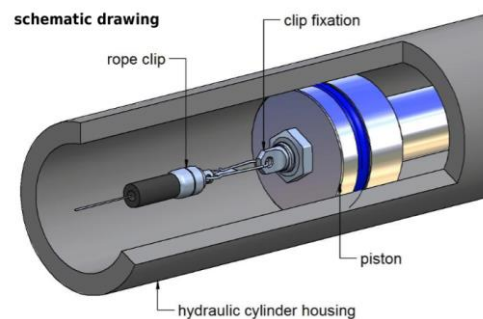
Detalhe fixação cabo ao êmbolo do SX300 (retirado de <http://www.waycon.biz>)
